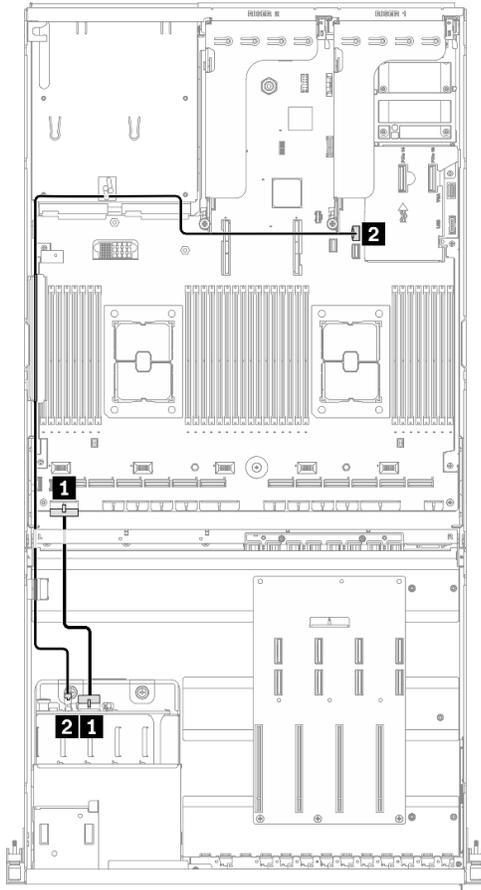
Instradamento dei cavi del backplane dell'unità - Configurazione B
